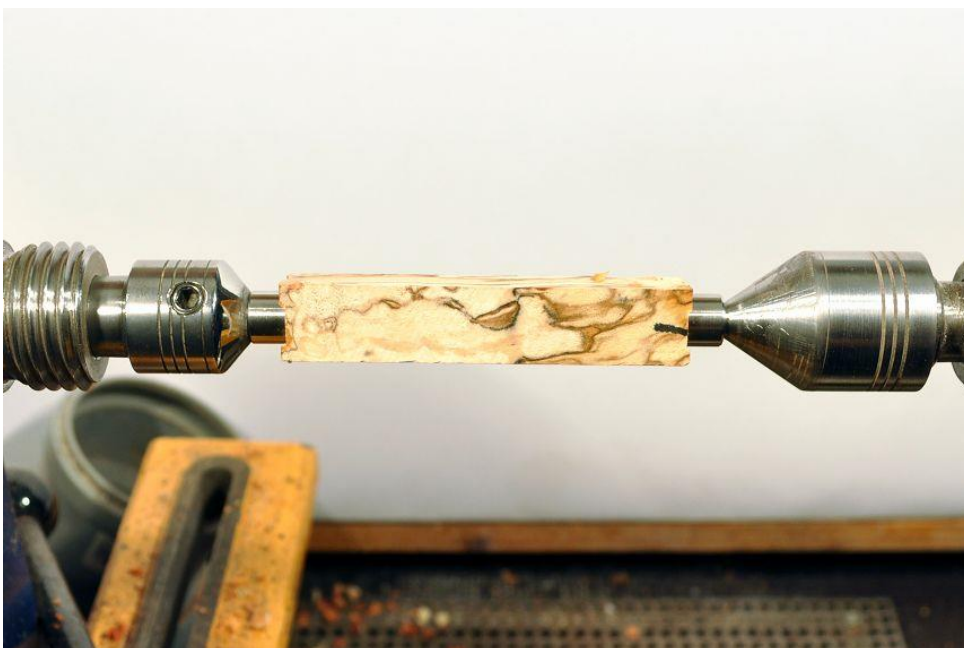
Mandrelstab soweit in das Mandrel einschieben, dass der Bushing noch auf dem Gewindefreien Stab-Stück halt findet.
